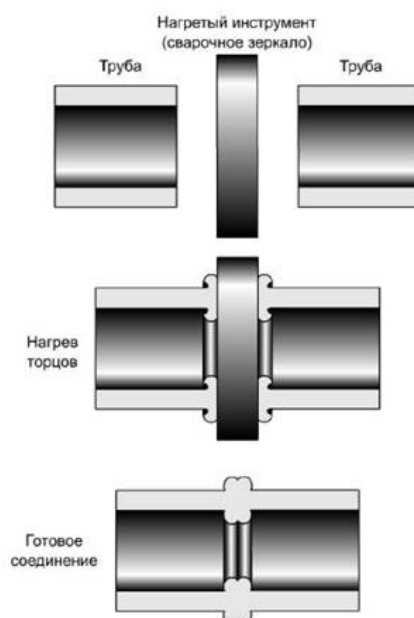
Сварка встык нагретым инструментом
